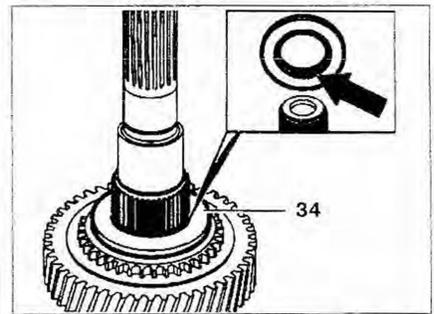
Упорная прокладка 34 при сборке закругленной поверхностью должна быть направлена вниз (стрелка).
